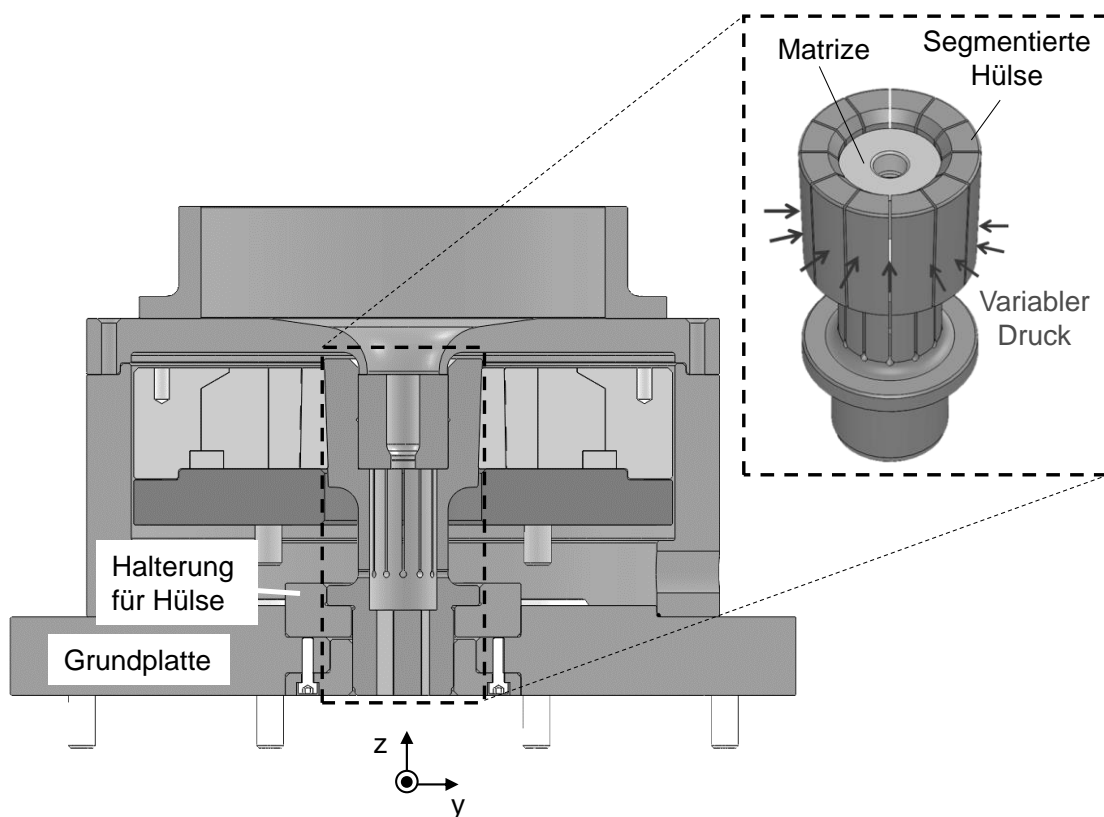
Werkzeugkomponenten für das Verjüngen.
